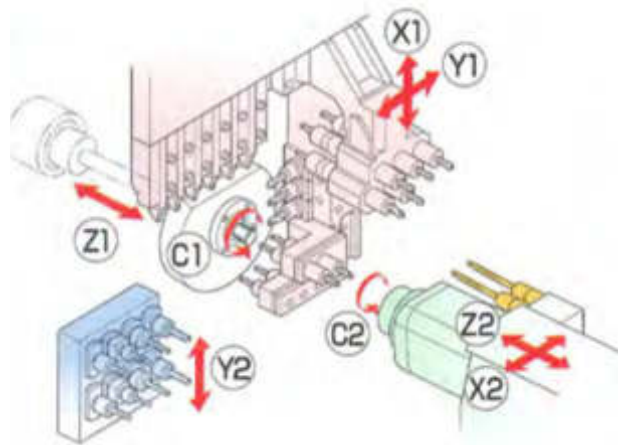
Схема внутрішнього оснащення для закріплення інструментів
